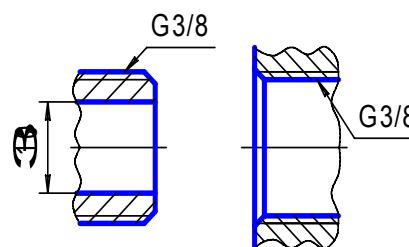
Примеры обозначения трубной цилиндрической резьбы
